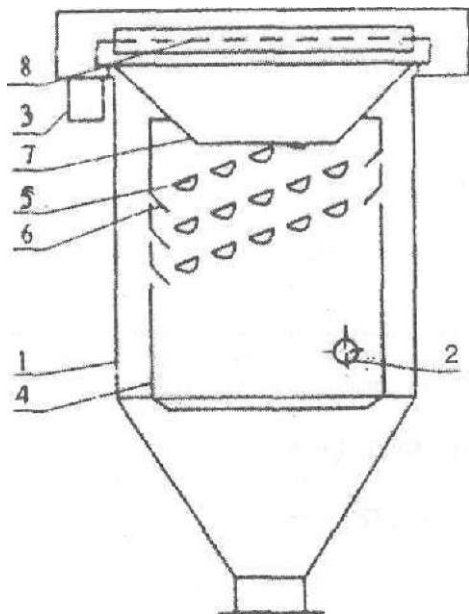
Конструкция гидроциклона для очистки сточных вод: 1 - цилиндрический корпус; 2, 3 - патрубки; 4 - внутренний цилиндр; 5 - отверстия; 6 - язычки; 7 - диафрагма; 8 - нефтесборник
